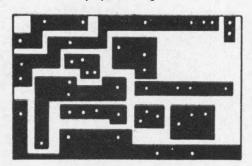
Plaqueta de circuito Impresso do amplificador, mostrando a face cobreada.
